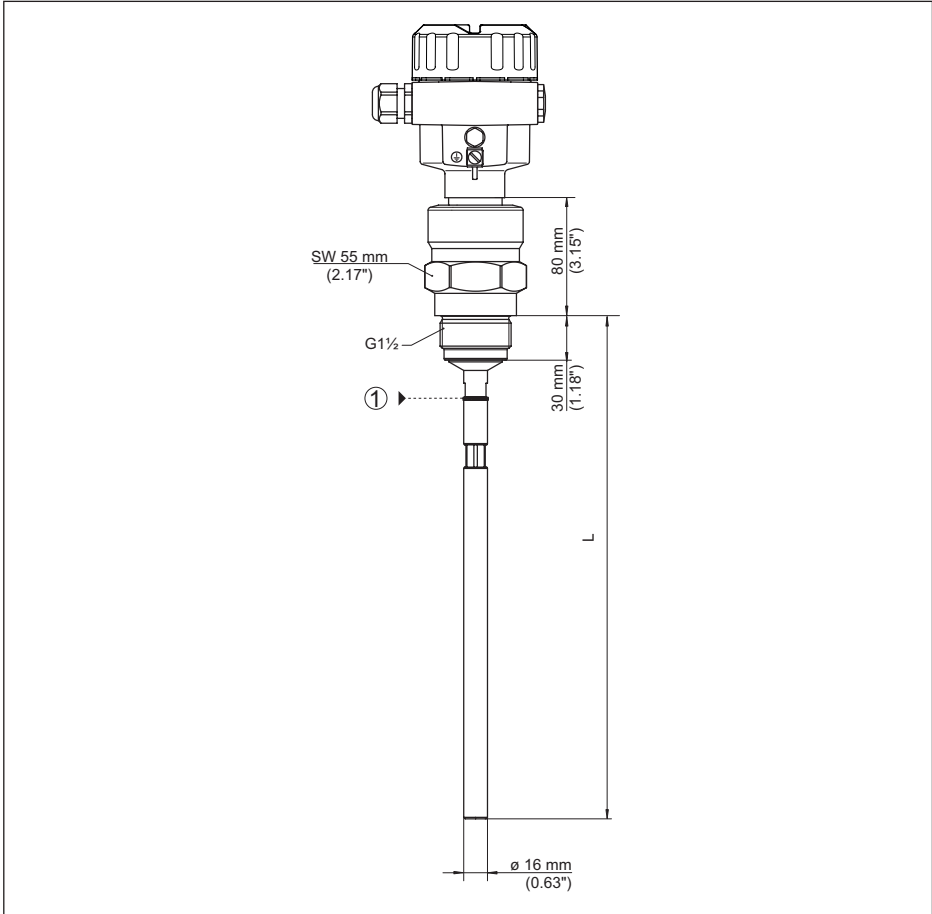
NivoGuide 3100, Stab ø 16 mm (0.63 in), Gewindeausführung
